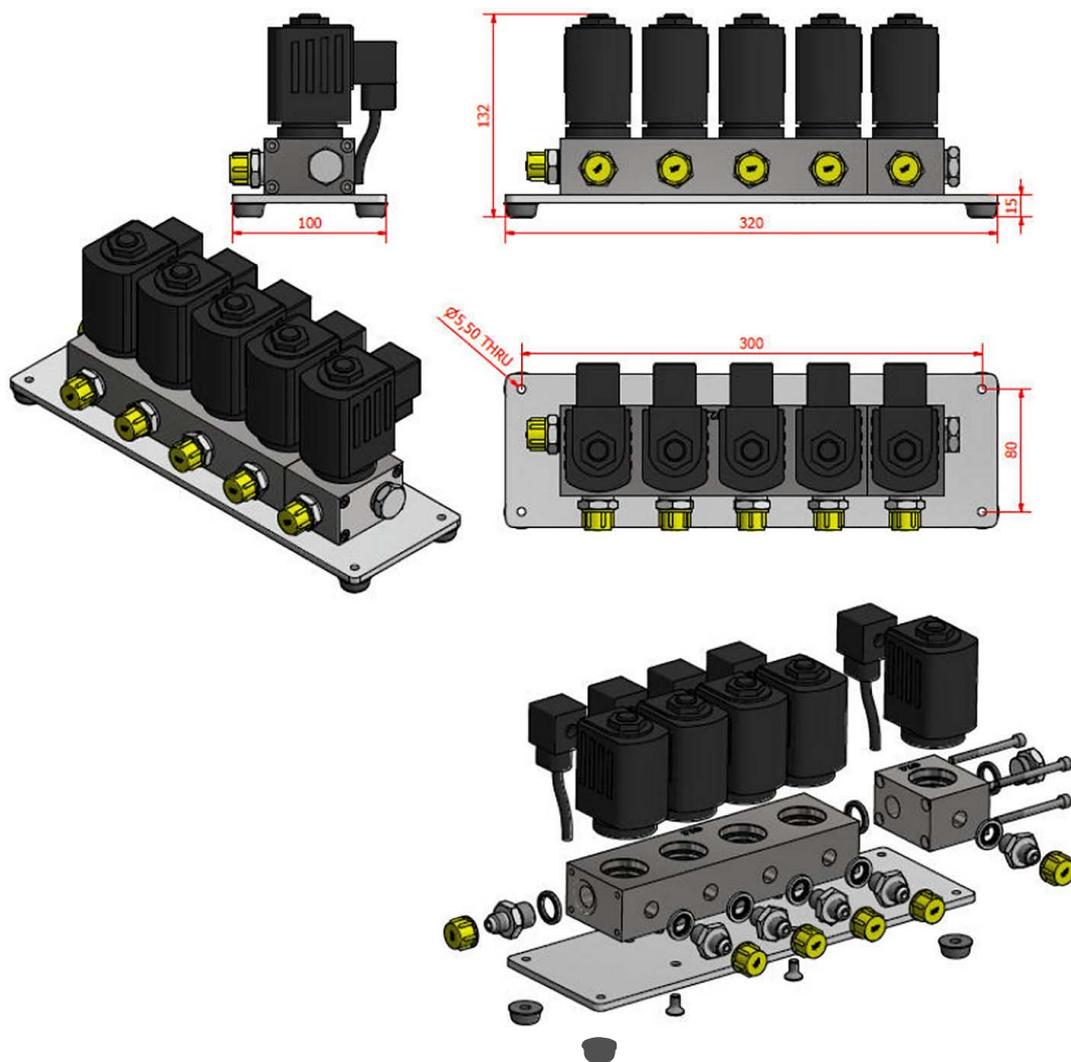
Dimensions du bloc de vannes 4+1 INDUCT (en mm)
